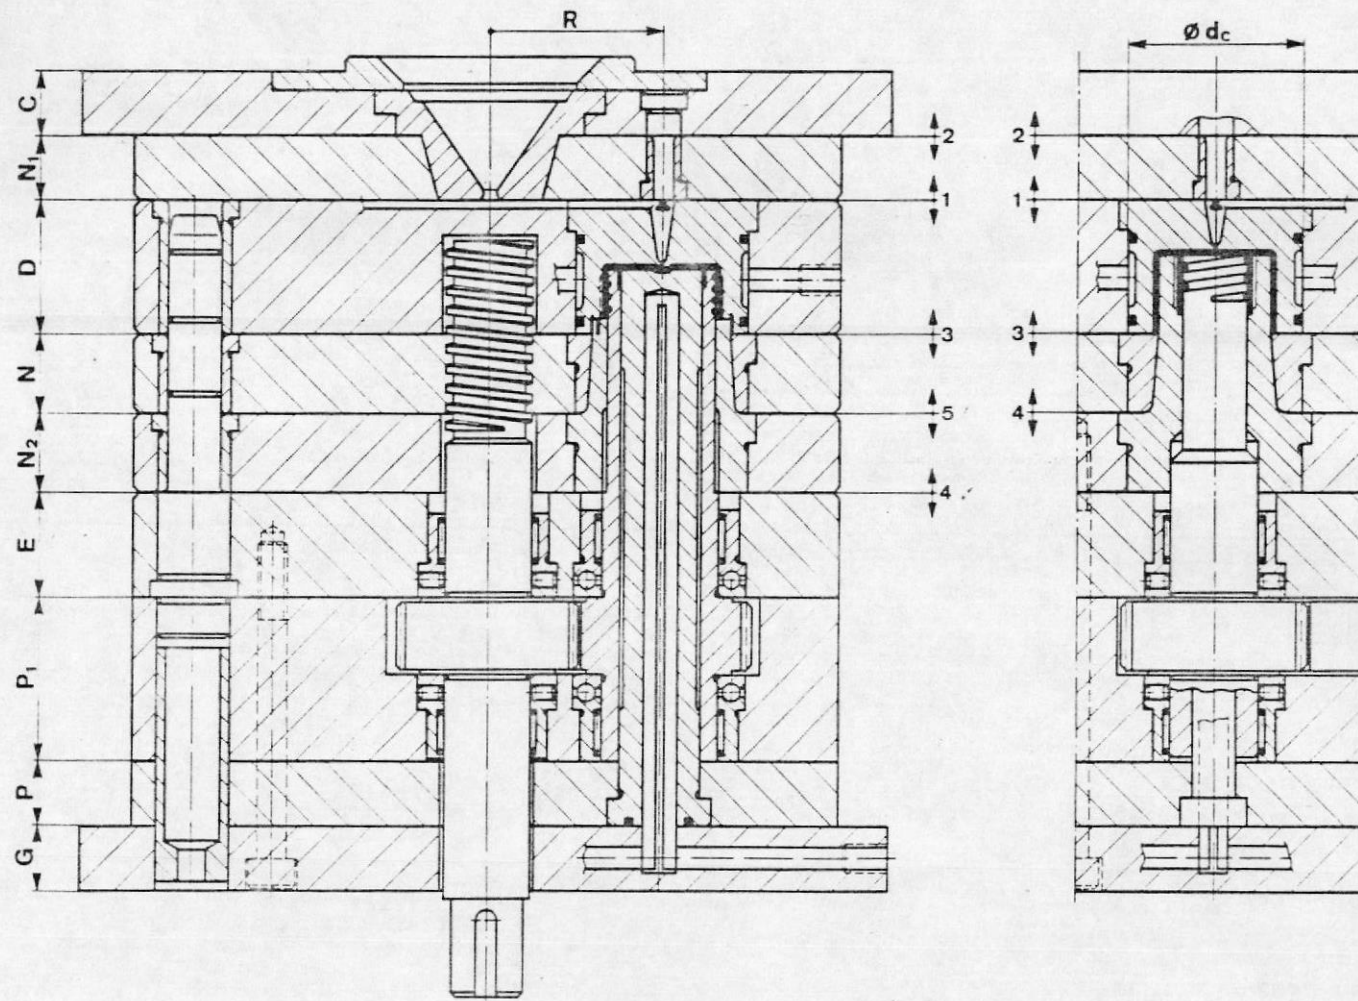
Molde desenroscado automático expulsión por placa expulsora.
